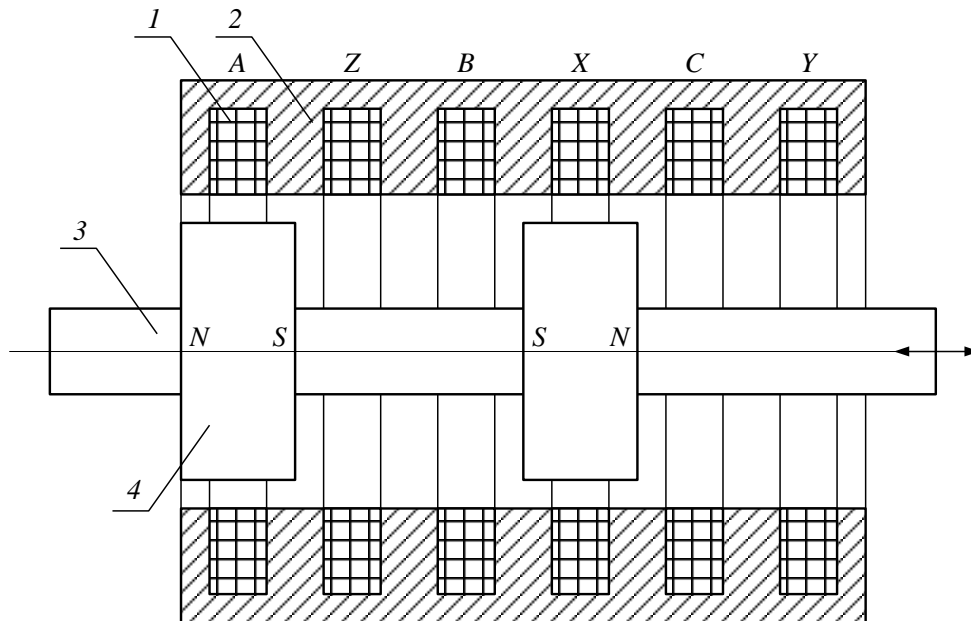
Конструктивна схема лінійного коаксіального двигуна
